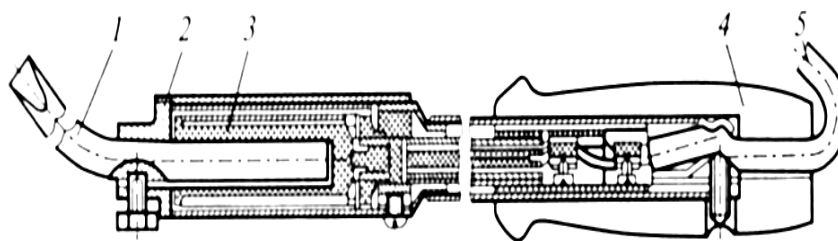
Электросварщик со сменным нагревательным элементом: 1-наконечник; 2-корпус; 3 - сменный нагревательный элемент; 4-ручка; 5-провода питания
